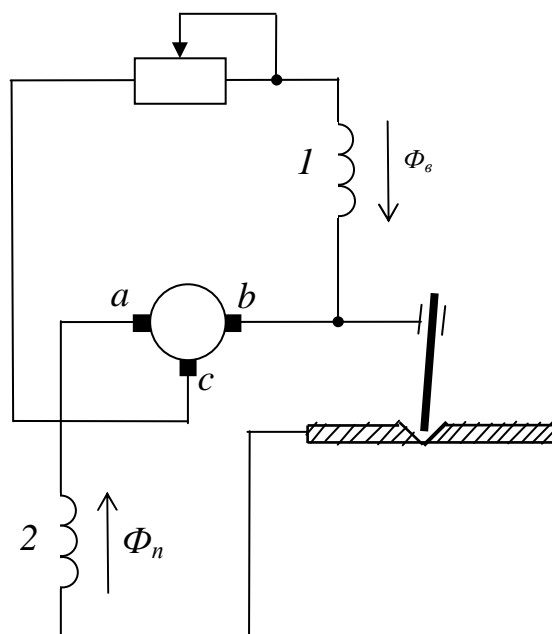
Сварочный генератор с размагничивающим действием реакции якоря:
